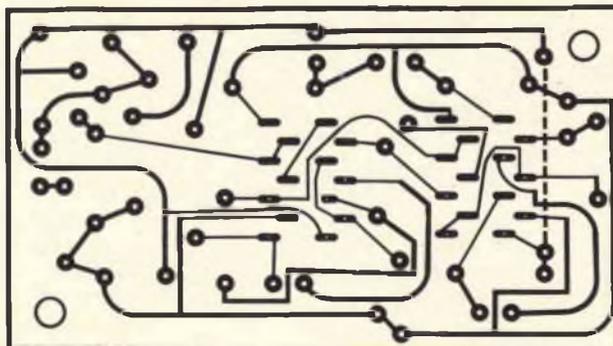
Disegno delle piste della basetta stampata di cui alla fig. 6.
